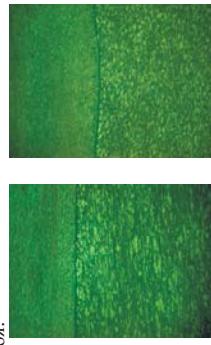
Граница контакта двух слоев выдавленной заготовки компрессорной лопатки №500:
